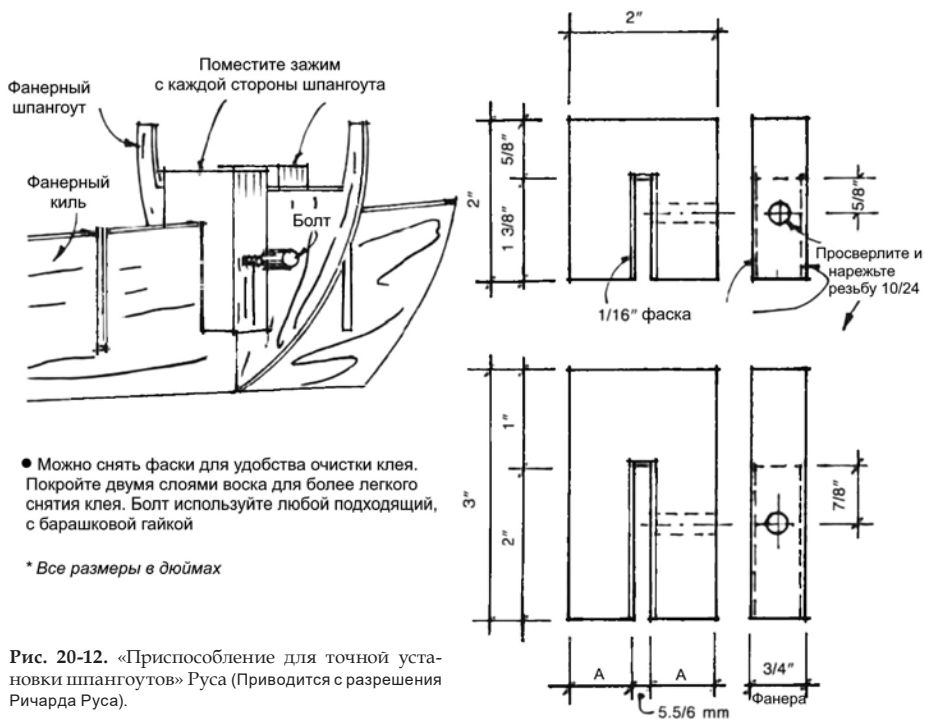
«Приспособление для точной установки шпангоутов» Руса (Приводится с разрешения Ричарда Руса).
